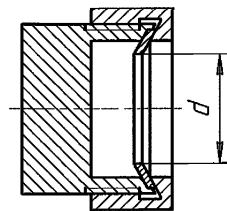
Приспособление для окончательной обработки  $d$
